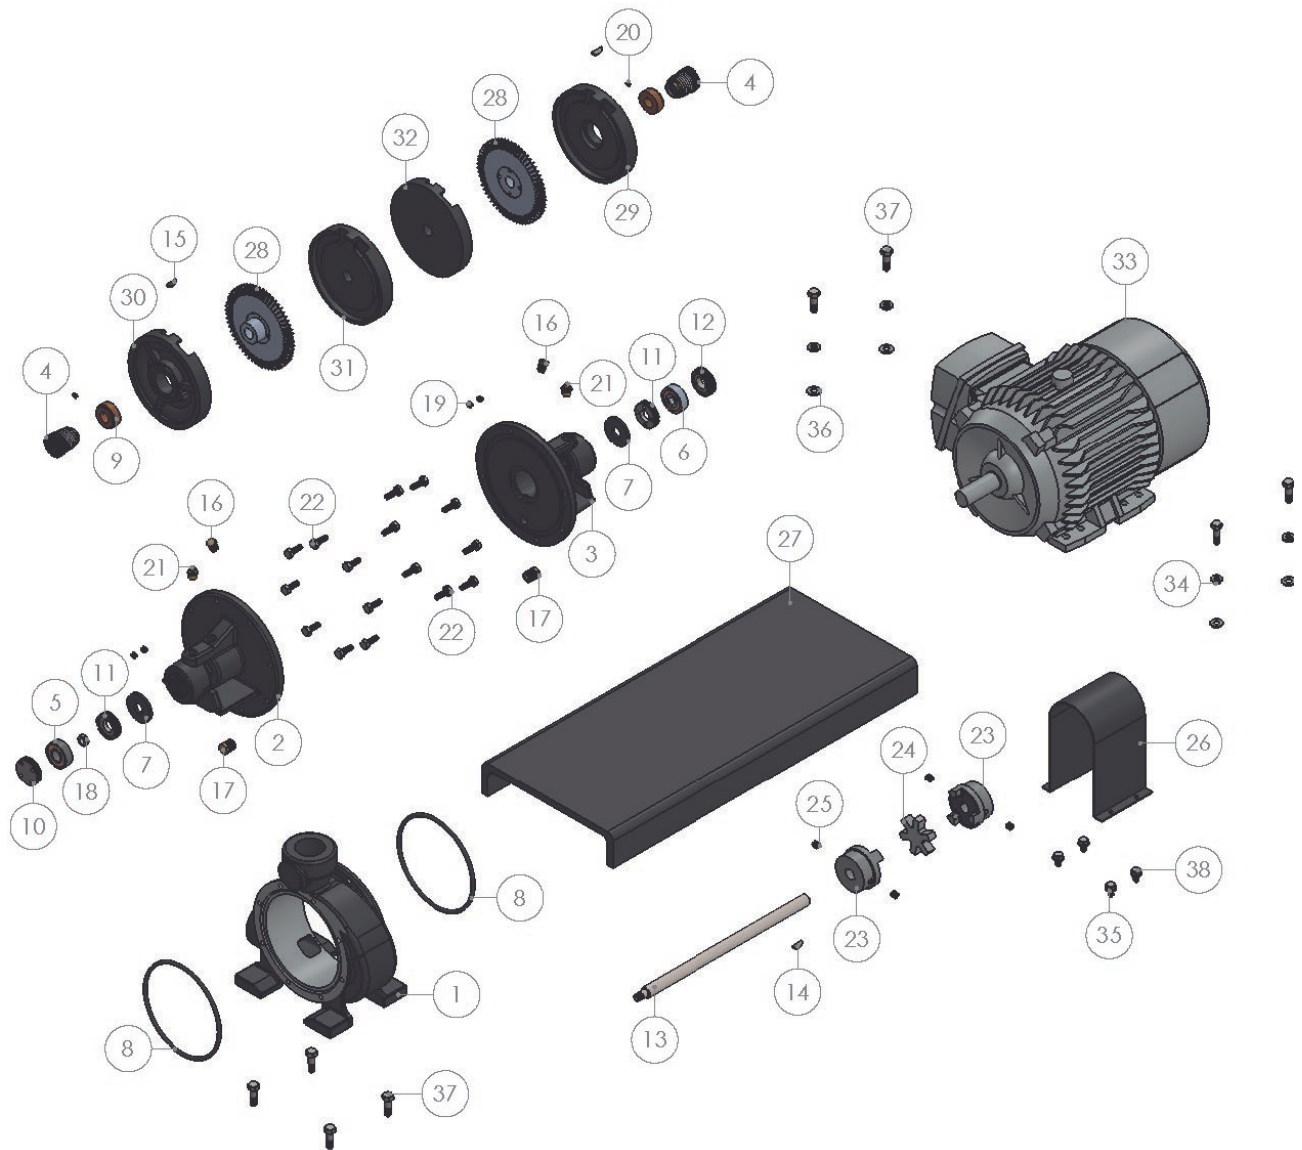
Vista del explosivo de la bomba (Sello mecánico)
